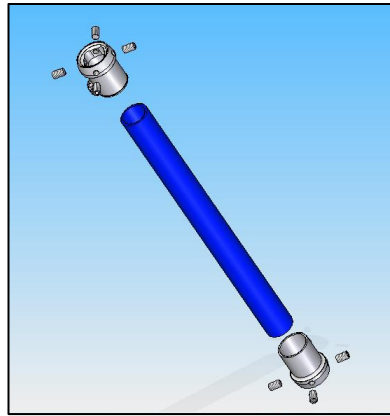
Vista explosionada del mecanismo de ayuda a la propulsión.
